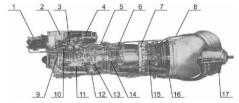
Двигатель ТВ2-117A (вид слева):
